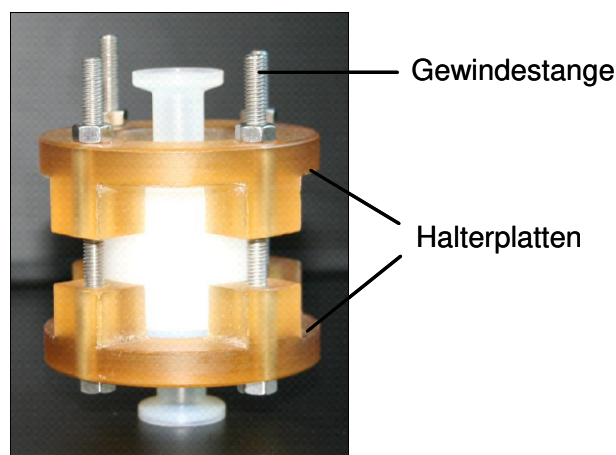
Wickeltestvorrichtung mit eingebautem Gehäuserohr und Gehäusekappen. Kappen und Rohr wurden durch Halterplatten und Gewindestangen unter Einsatz von O-Ringen, die sich zwischen Rohr und Kappe befanden, fixiert und abgedichtet
